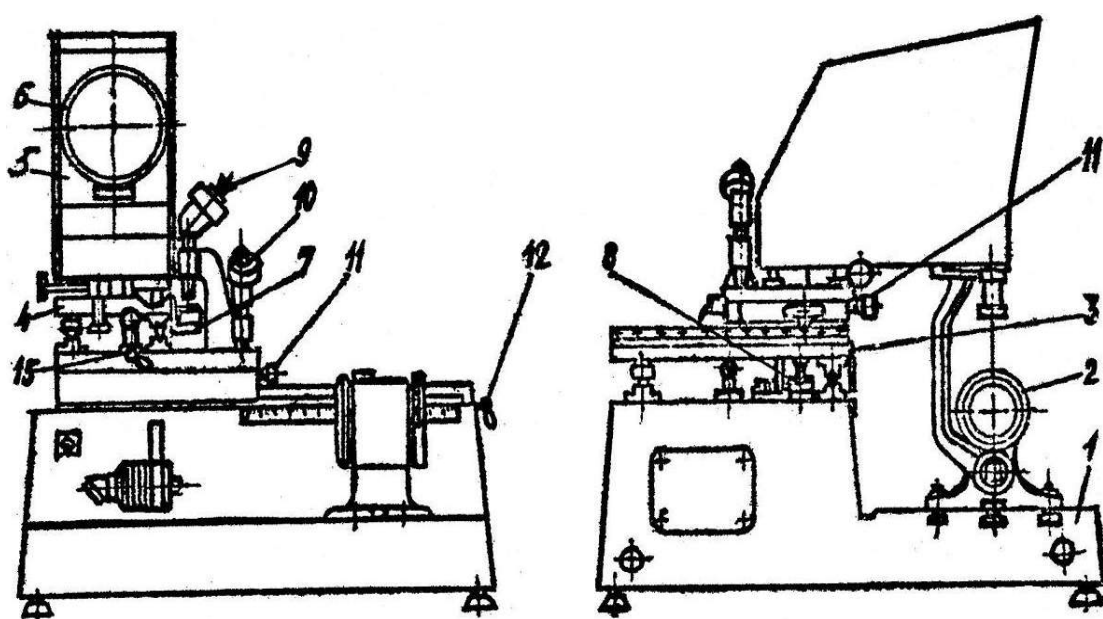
Эскиз прибора модели БВ-2010 для размерной настройки инструмента
